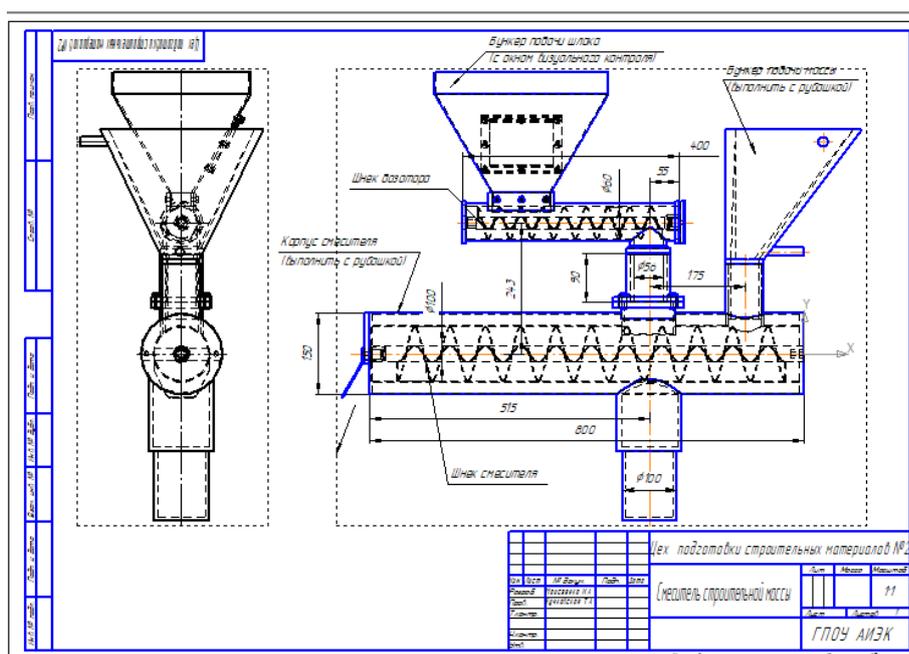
Смеситель строительной массы – сборочный чертеж
